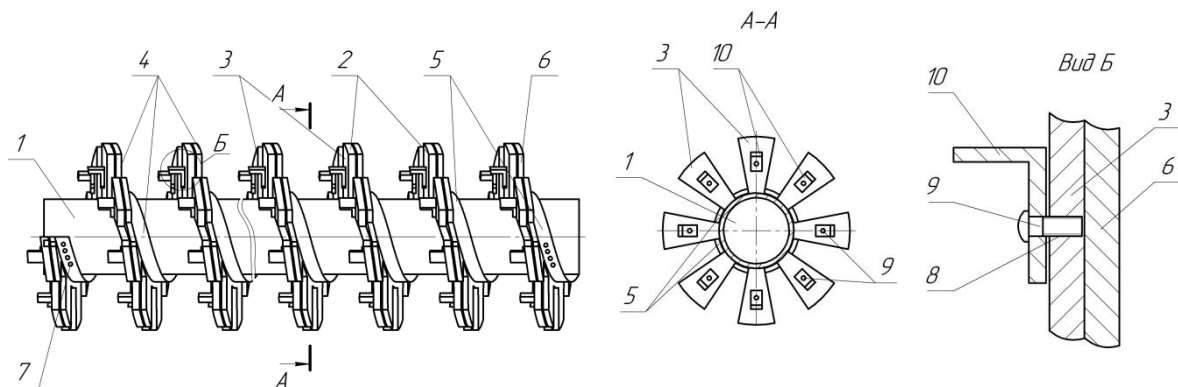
Гвинтовий робочий орган змішувача: 1 - вал; 2 - гвинт; 3 - нерухома лопатева спіраль; 4 - рухома лопатева спіраль; 5 - суцільна внутрішня циліндрична частина спіралі 4; 6 - лопатева зовнішня частина спіралі 4; 7 - гвинти зміни положення; 8 - кріпильні отвори; 9 - кріпильні гвинти; 10 - елементи Г-подібної форми
